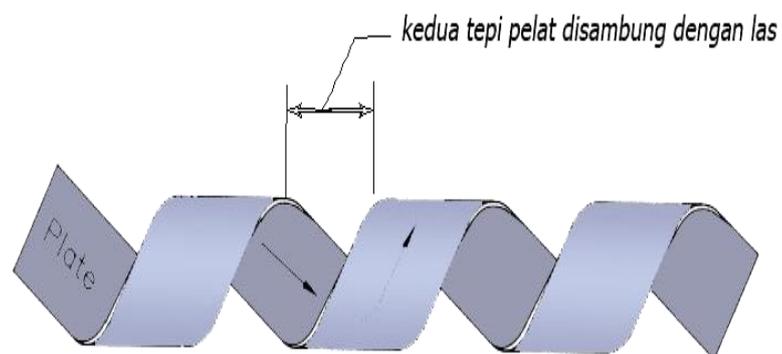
Pipa hasil Butt-welded Pipe
